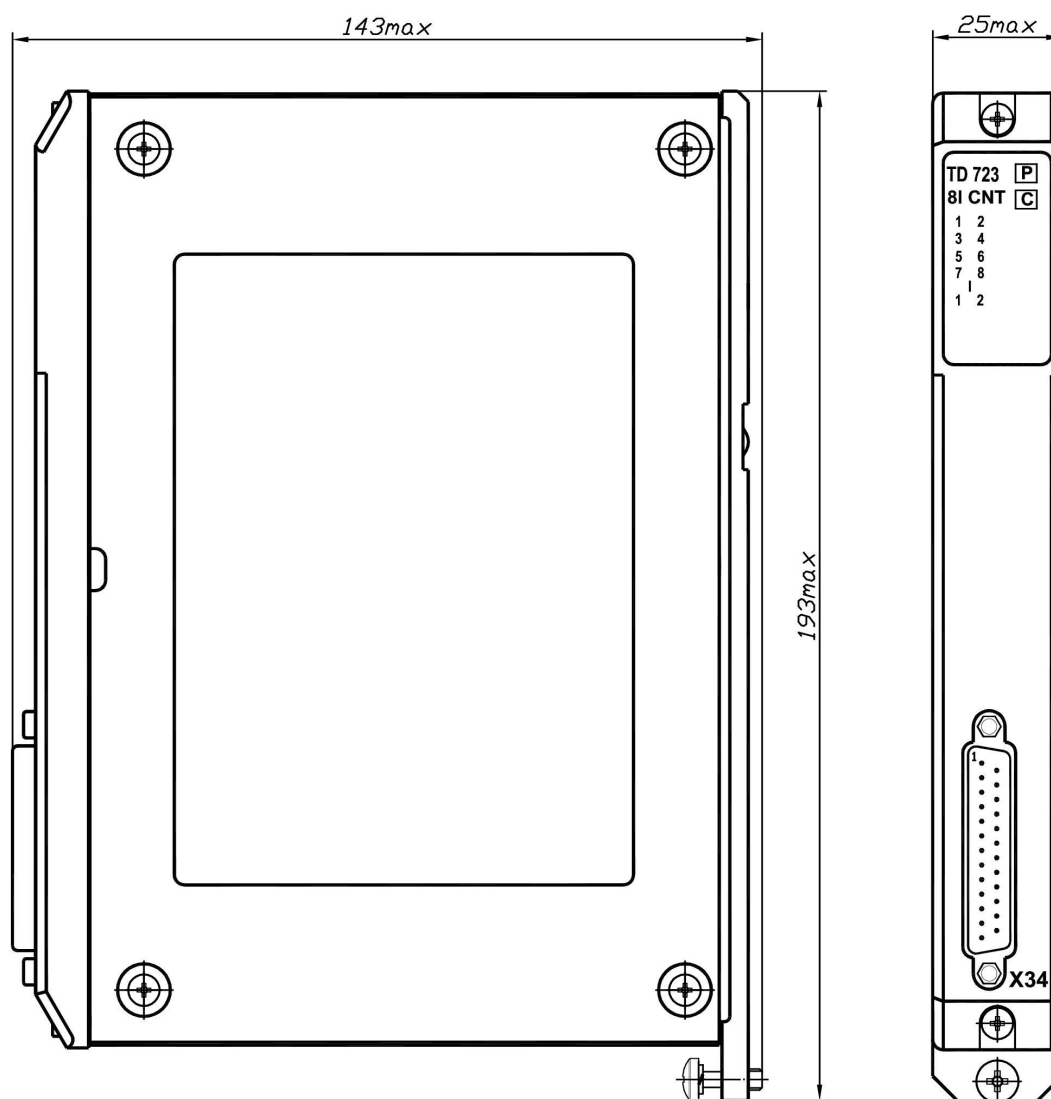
Габаритный чертеж модуля исполнения TD 723 8I CNT
